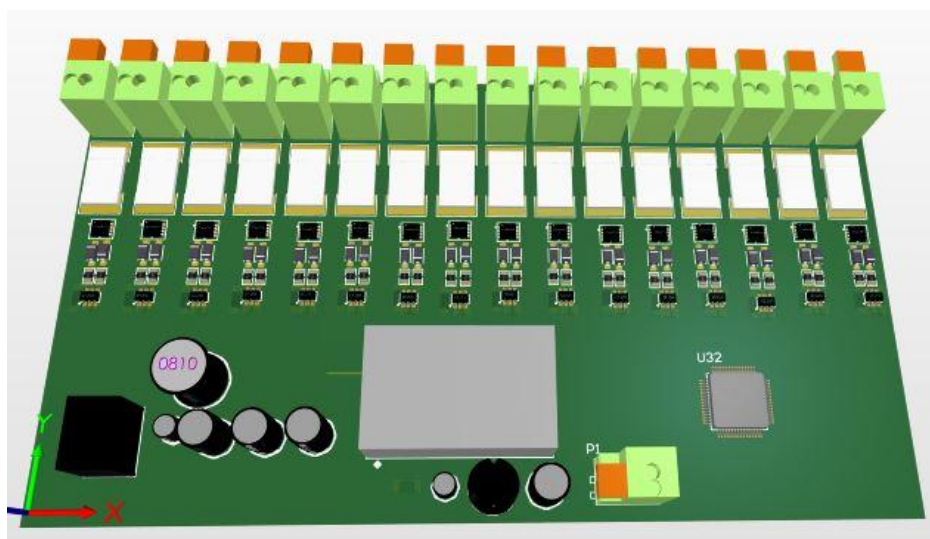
Visualización 3D de la PCB del sistema de balanceado desarrollado.
